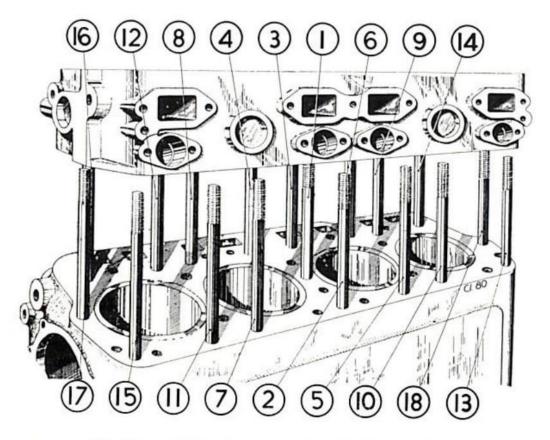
Ordre de serrage des écrous de cu'asse.
